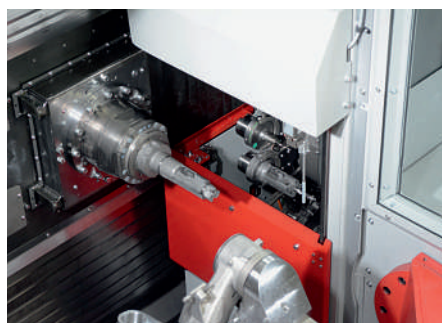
SYNCROMILL D – Bearbeitungsraum mit Werkzeugwechsel
